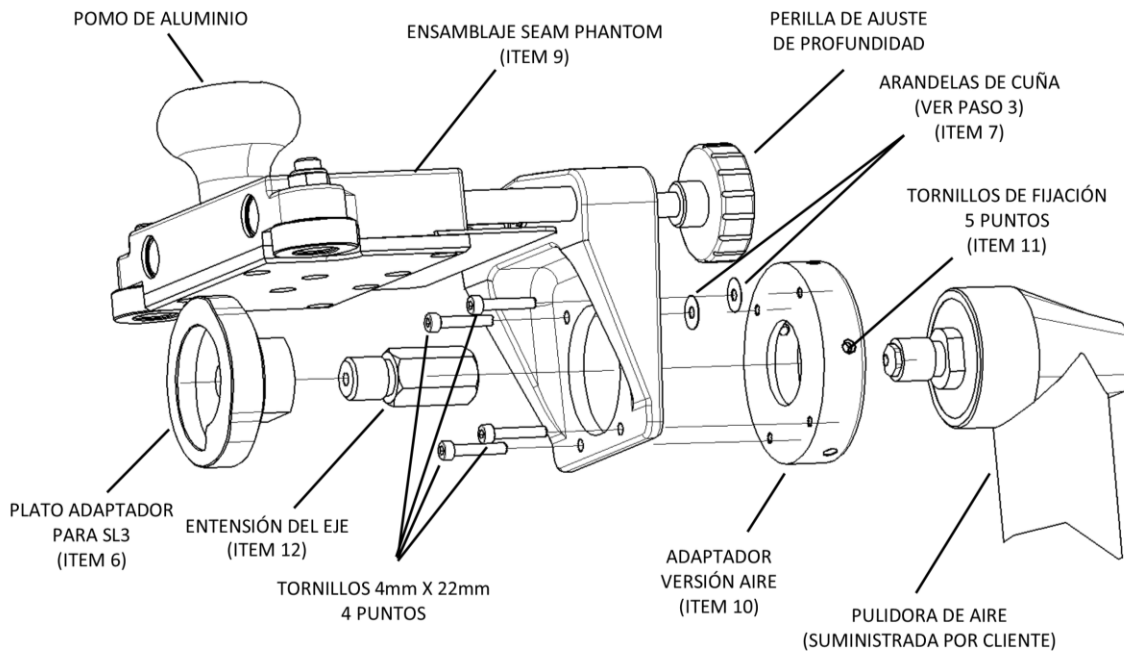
Vista aumentada de montaje de la versión Aire
